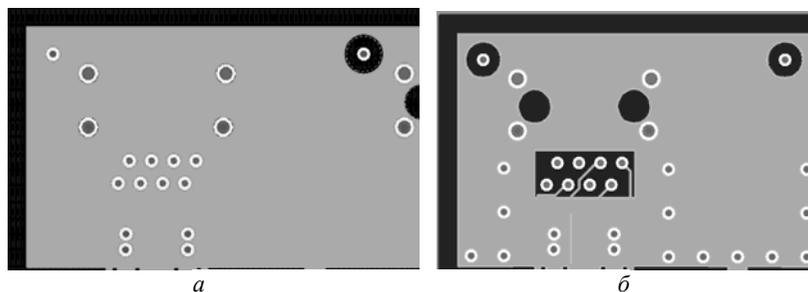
Фрагменты ПП: предыдущей (а) и новой, с дополнительными металлизированными отверстиями (б)
